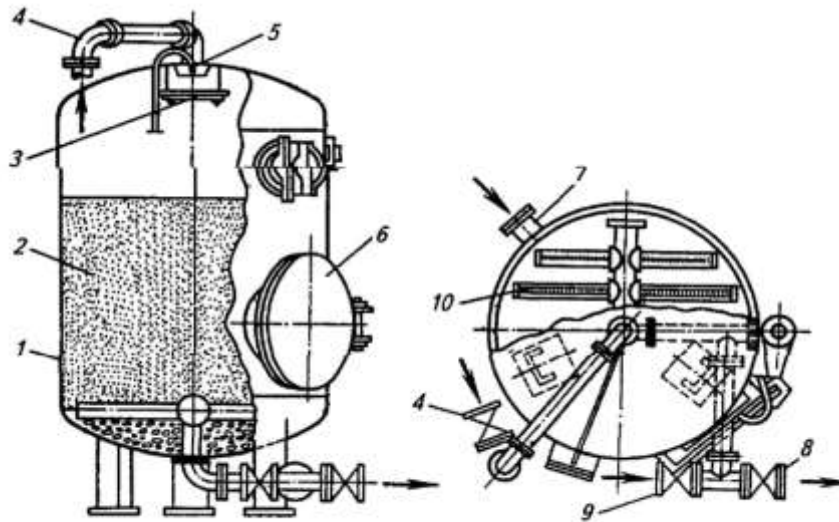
Сорбционный вертикальный параллельно-проточный фильтр: 1 – корпус; 2 – неподвижный слой активного угля; 3 – отбойник; 4 – трубопровод подачи очищаемой сточной воды; 5 – труба сброса воздуха; 6 – люк; 7 – трубопровод для выгрузки активного угля; 8 – трубопровод отвода очищенной воды; 9 – трубопровод подачи взрыхляющей воды; 10 – распределительная система труб
